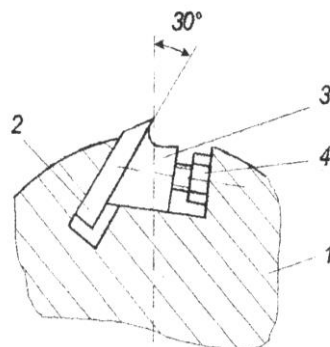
Схема закріплення ножа у фрезі для плоского фрезування: 1 - корпус фрези; 2 - ніж; 3 - клин; 4 – болт
